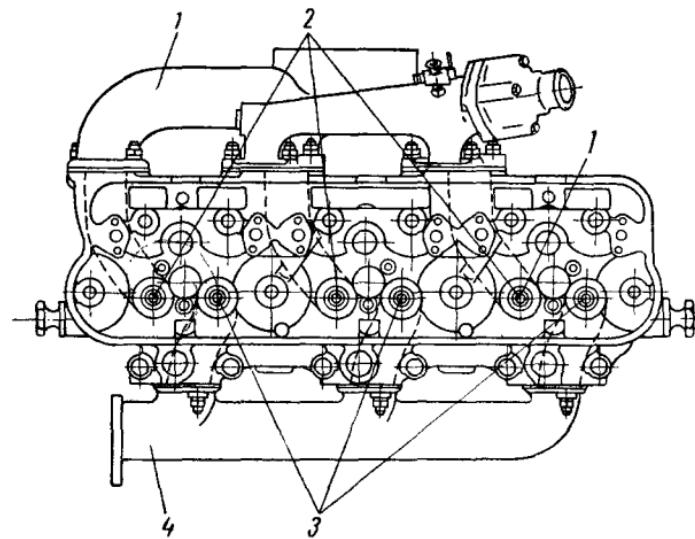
Схема расположения клапанов правого ряда цилиндров:
